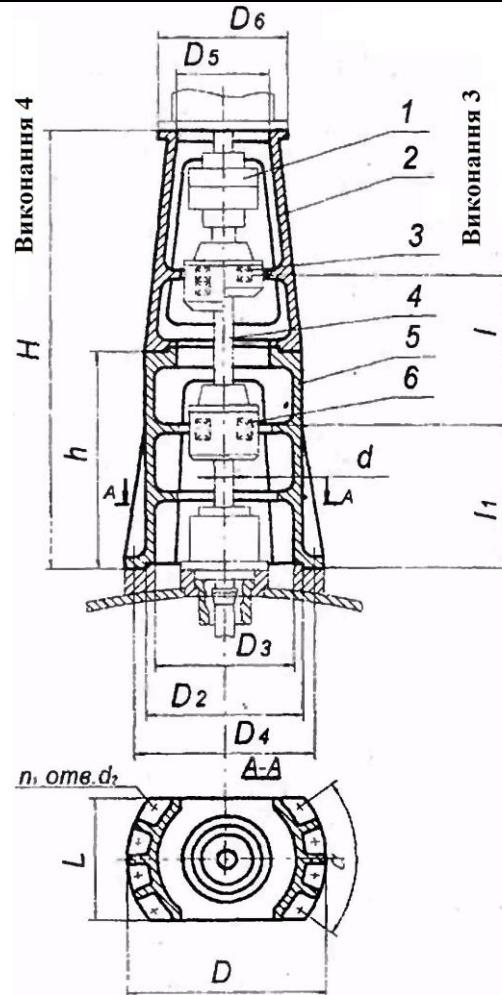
Вертикальна стійка 1-го типу, виконання 3 та 4 [4]: 1 – муфта пружна МУВП; 2 – стійка верхня; 3 – підшипник радіально-упорний; 4 – вал; 5 – стійка нижня; 6 – підшипник самоустановлювальний дворядний
